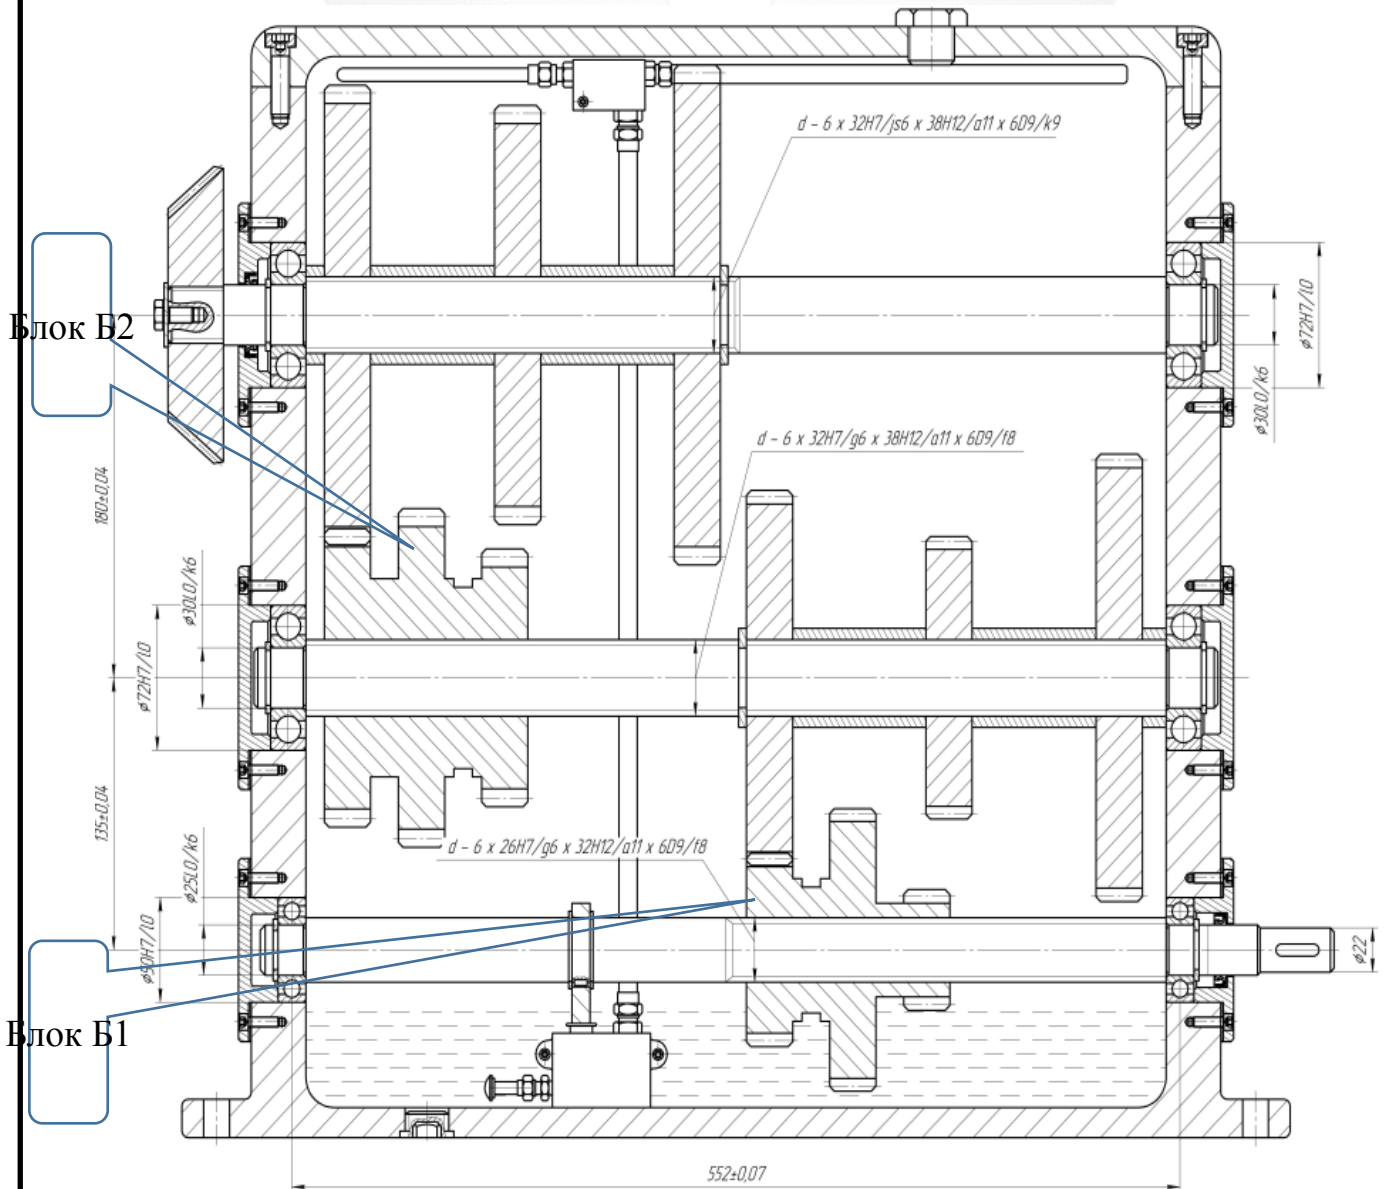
Конструкція коробки швидкостей модернізованого привода головного руху верстата.
